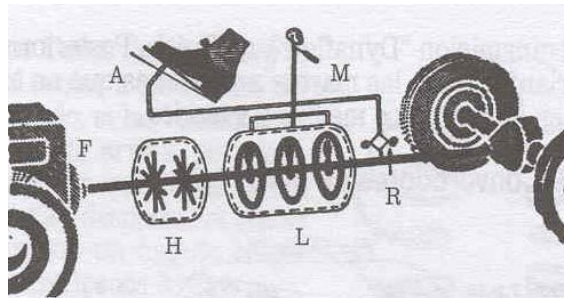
Cambio con turbo-embrague y engranajes planetarios
